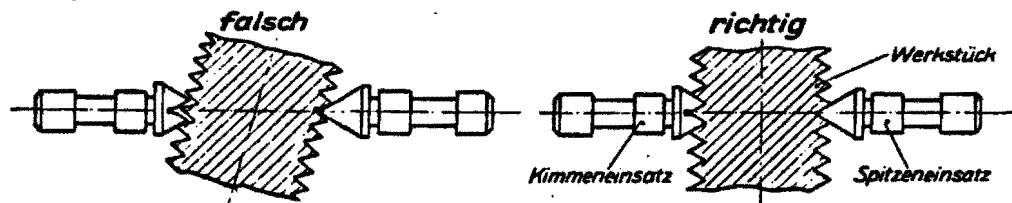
Gewinde-Schraublehre 25 bis 50 mm mit Prüfmaß 60°
